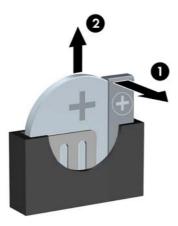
Extracción y reemplazo de una batería plana (Tipo 2)
